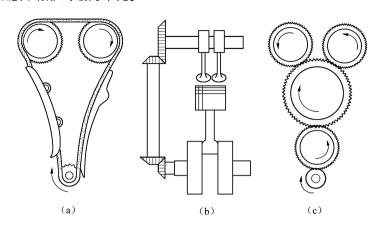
顶置凸轮轴式配气机构的传动形式 (a) 链传动;(b) 锥齿轮传动;(c) 圆柱齿轮传动
